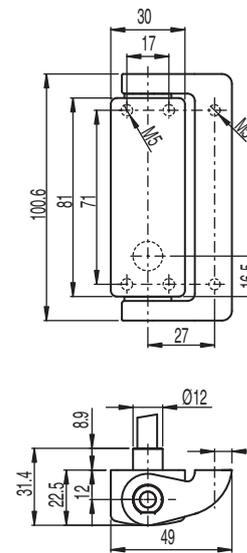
Dimensões do S400-M4-CB2PUR-W em mm
